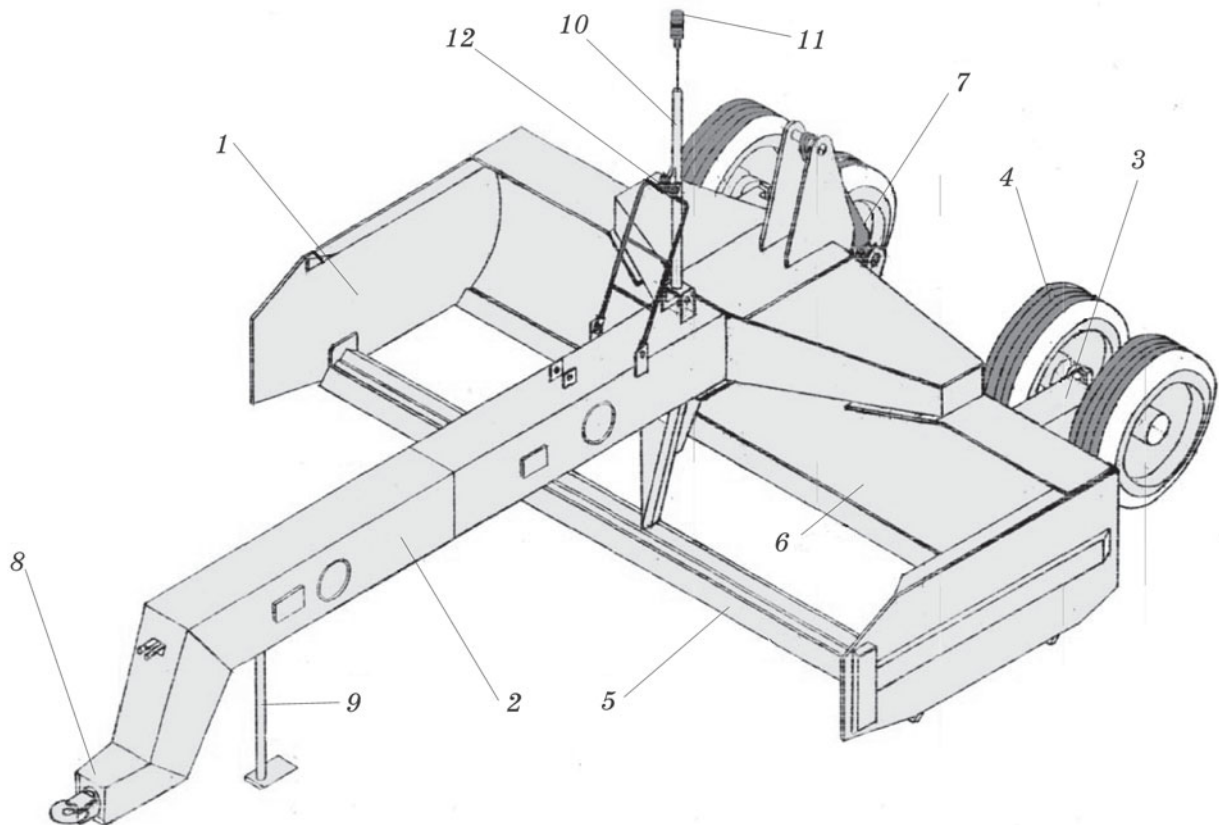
Короткобазовый автоматизированный планировщик ПАУ-4,2Р: 1 – ковш; 2 – несущая рама; 3 – задний мост; 4 – колеса; 5 – рыхлитель; 6 – нож; 7 – гидроцилиндр; 8 – сцепное устройство; 9 – домкрат; 10 – телескопическая стойка; 11 – лазерный приемник; 12 – лестница
